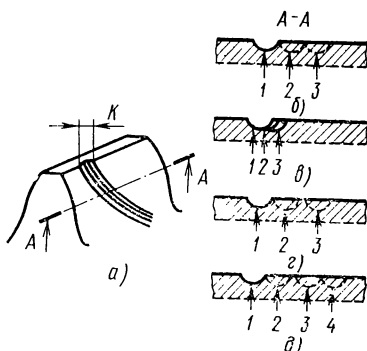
Влияние расположения режущих зубчиков шевера на шероховатость поверхности:
